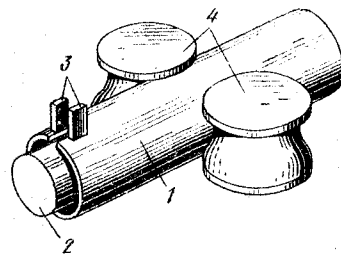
Схема сварки труб с подводом тока контактами:
